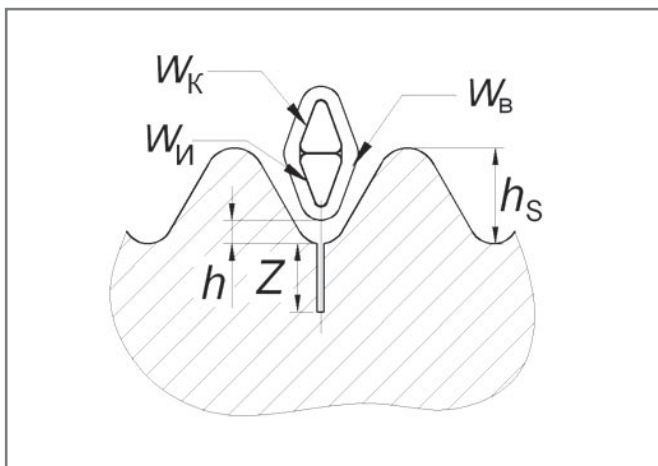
ВТП с обмотками, повторяющими форму профиля резьбы, расположенными над впадиной резьбы тангенциально.
